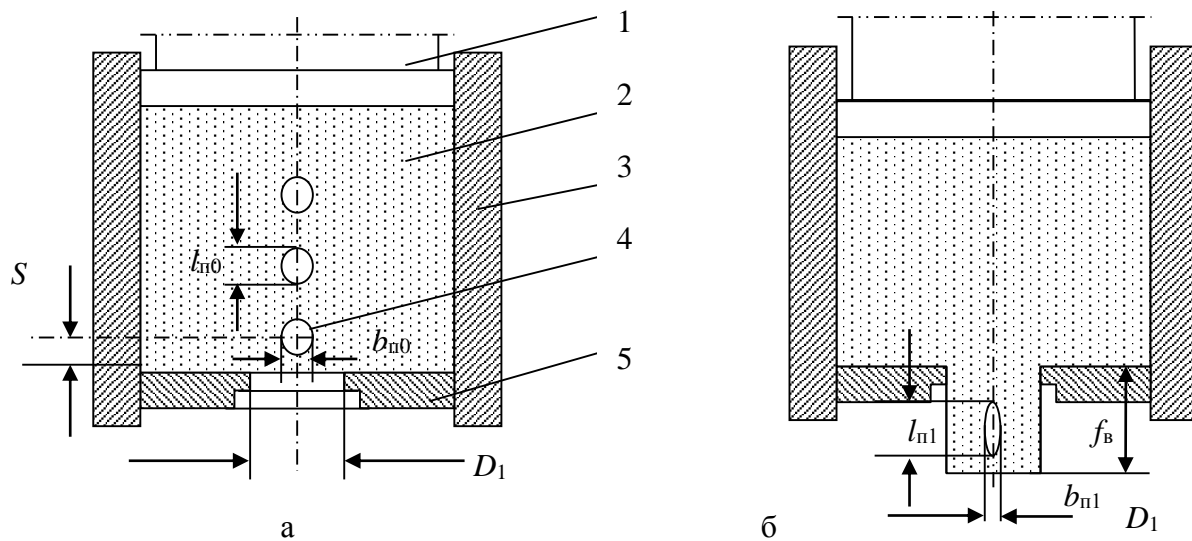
Схема прессования круглого прутка с расположенными по его оси порами: а – до прессования; б – после выдавливания части прутка на длину $l_{п1}$; 1 – пуансон; 2 – деформируемый металл; 3 – контейнер; 4 – пора; 5 – матрица
